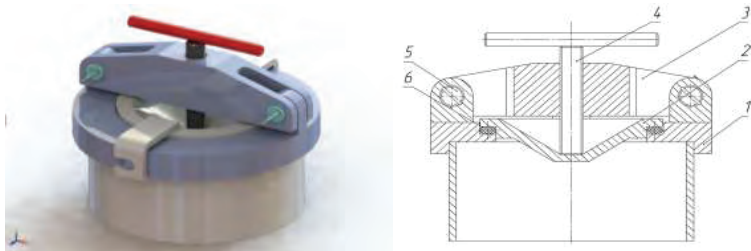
Конструкция концевой затвора: 1 - фланец; 2 - крышка; 3 - траверса; 4 - винт прижимной; 5 - ось; 6 - уплотнительный элемент.
